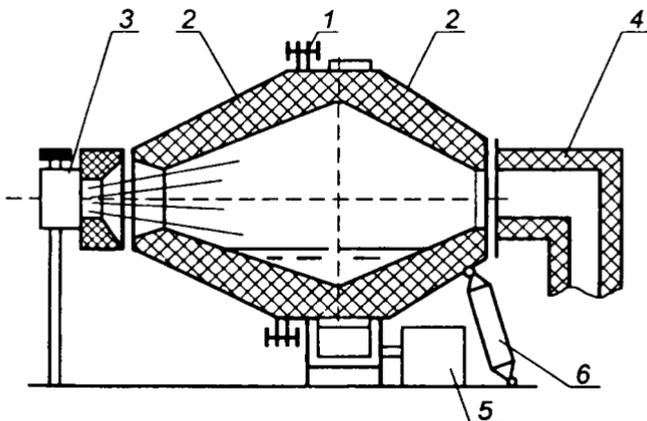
Схема вращающейся роторной печи для переплава алюминиевых отходов
